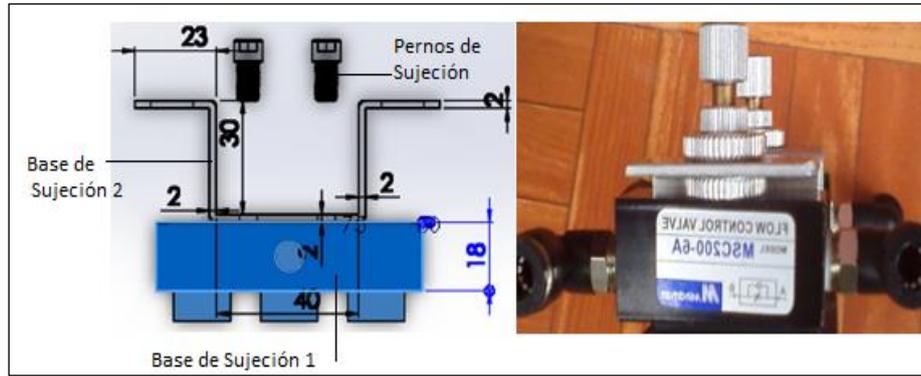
Elementos de fijación y válvula de estrangulamiento y atirretorno.
